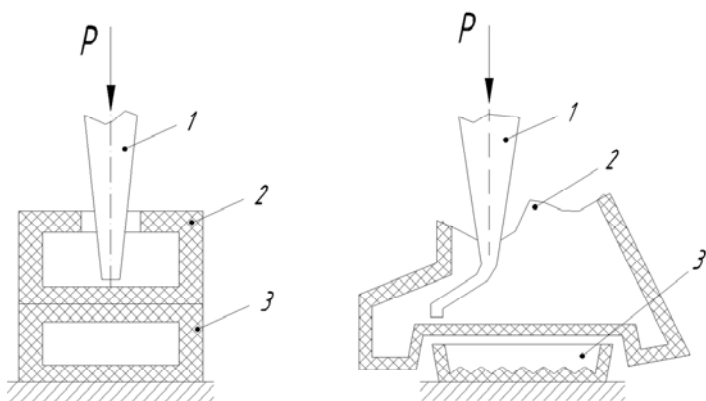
Схемы ультразвуковой сварки в труднодоступных местах:
